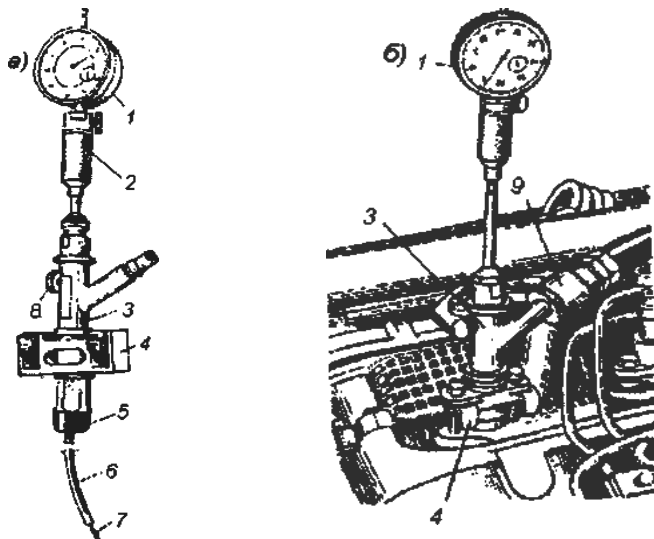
Пристрій КИ-11140-ГОСНІТІ для виміру зазорів у кривошипно-шатунному механізмі: а – загальний вид приладу; б – установка приладу на двигун
